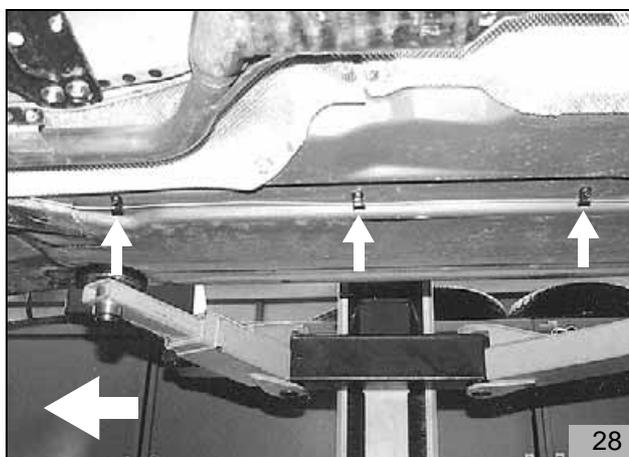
bis Bild 28 gültig für alle Fahrzeuge
